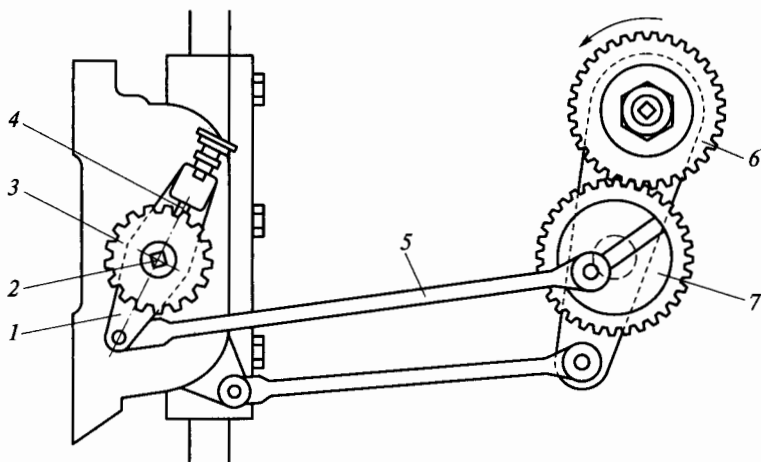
Схема механизма подачи стола поперечно-строгального станка
